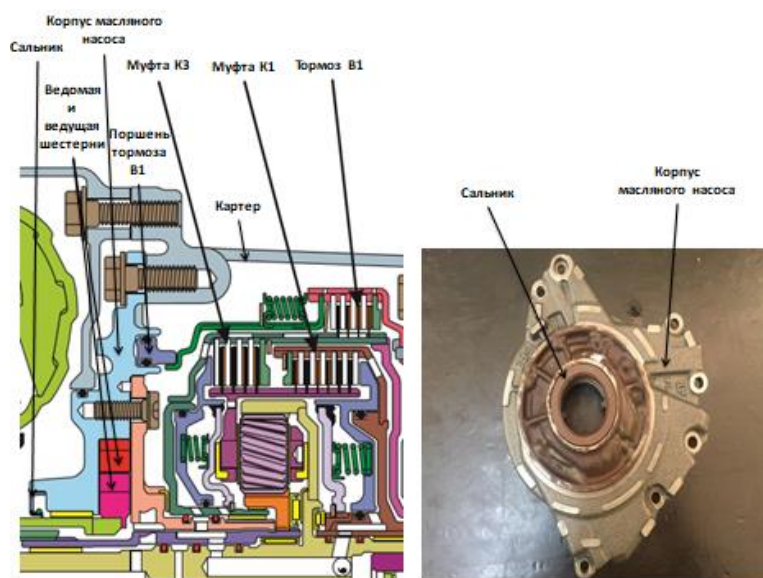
Устройство и назначение корпуса масляного насоса и сальника
